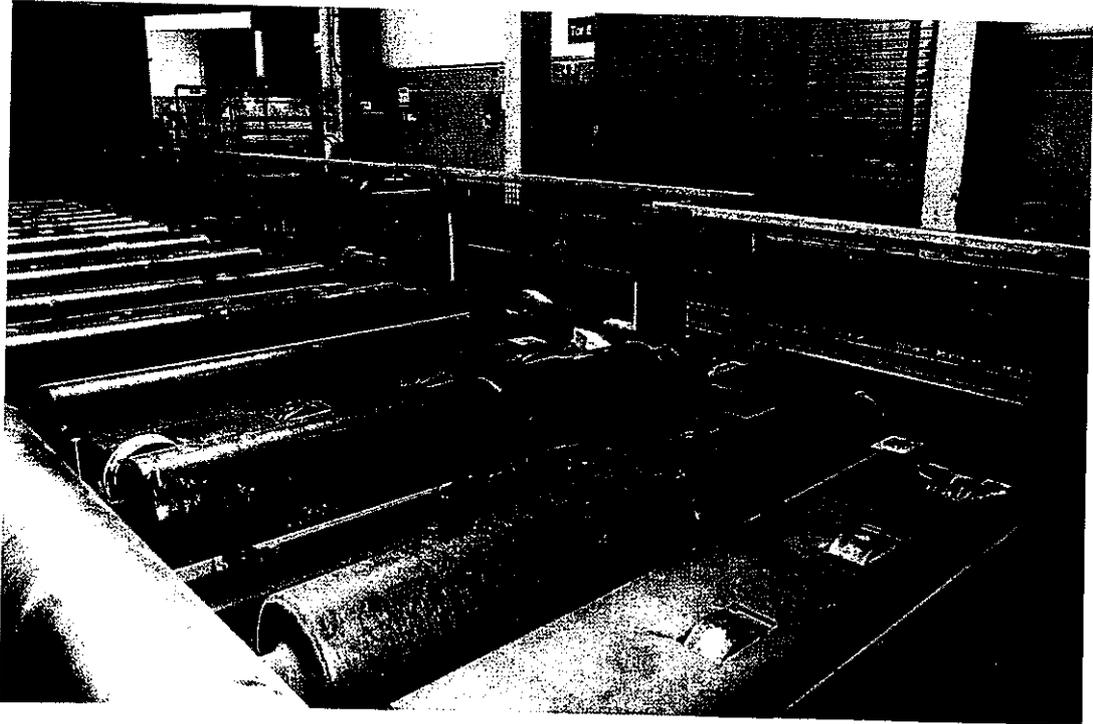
Hubbalken mit Positionssensoren für die Bleche und Anschlag zur Steuerung des Materialflusses entweder zur Sprühbeize oder zur Säge / mech. Bearbeitung
